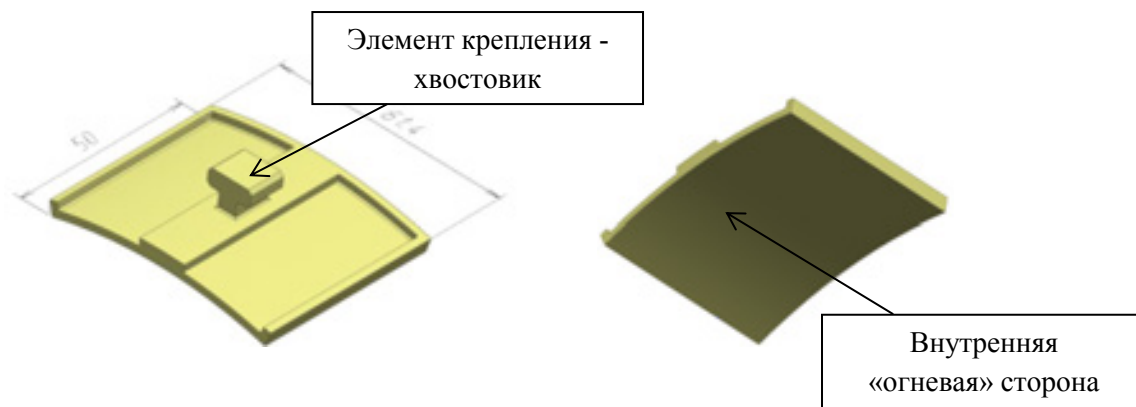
3D-модель прототипа элементов облицовки жаровой трубы из ККМ
